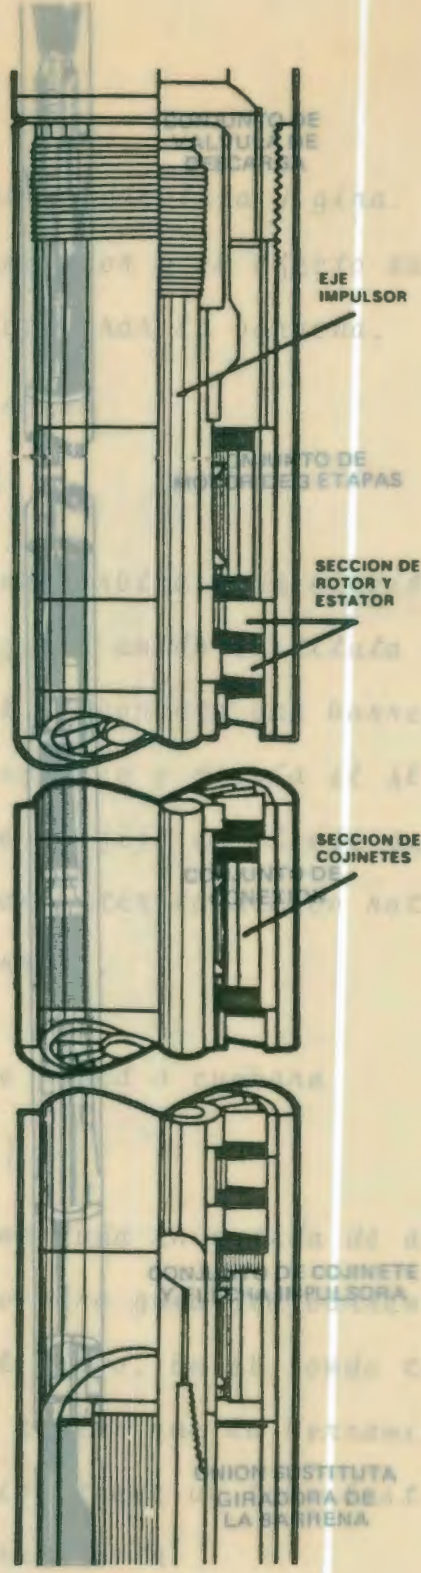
Componentes de un motor hidráulico de Fondo de Hoyo
